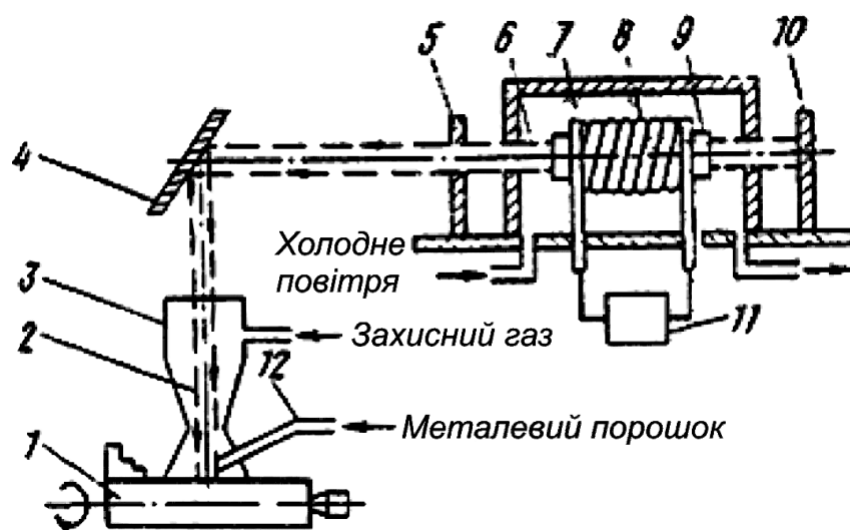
Схема установки для лазерного зварювання і наплавлення з рубіновим генератором
